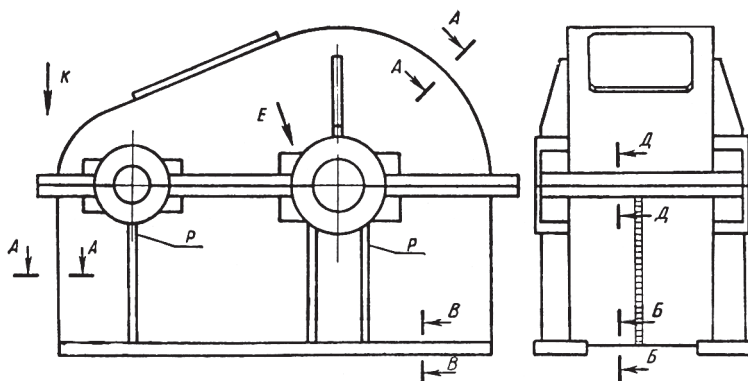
Определение конструктивных элементов сварного корпуса редуктора
